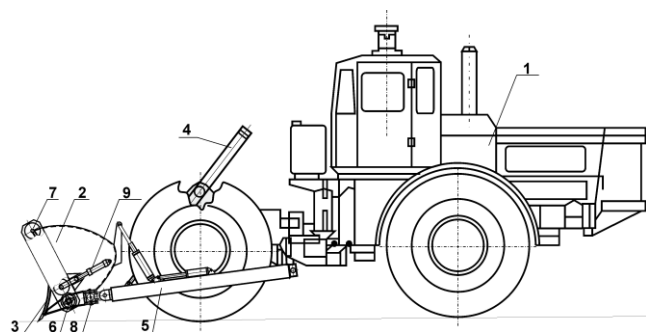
Бульдозер-погрузчик многоцелевого назначения с трансформирующимся рабочим оборудованием: 1-базовая машина; 2-ковш; 3-отвал; 4-гидроцилиндры подъема и опускания; 5-телескопические толкающие брусья; 6-роторный рабочий орган; 7-бортовой редуктор; 8-подвижной кронштейн; 9-направляющий гидроцилиндр
